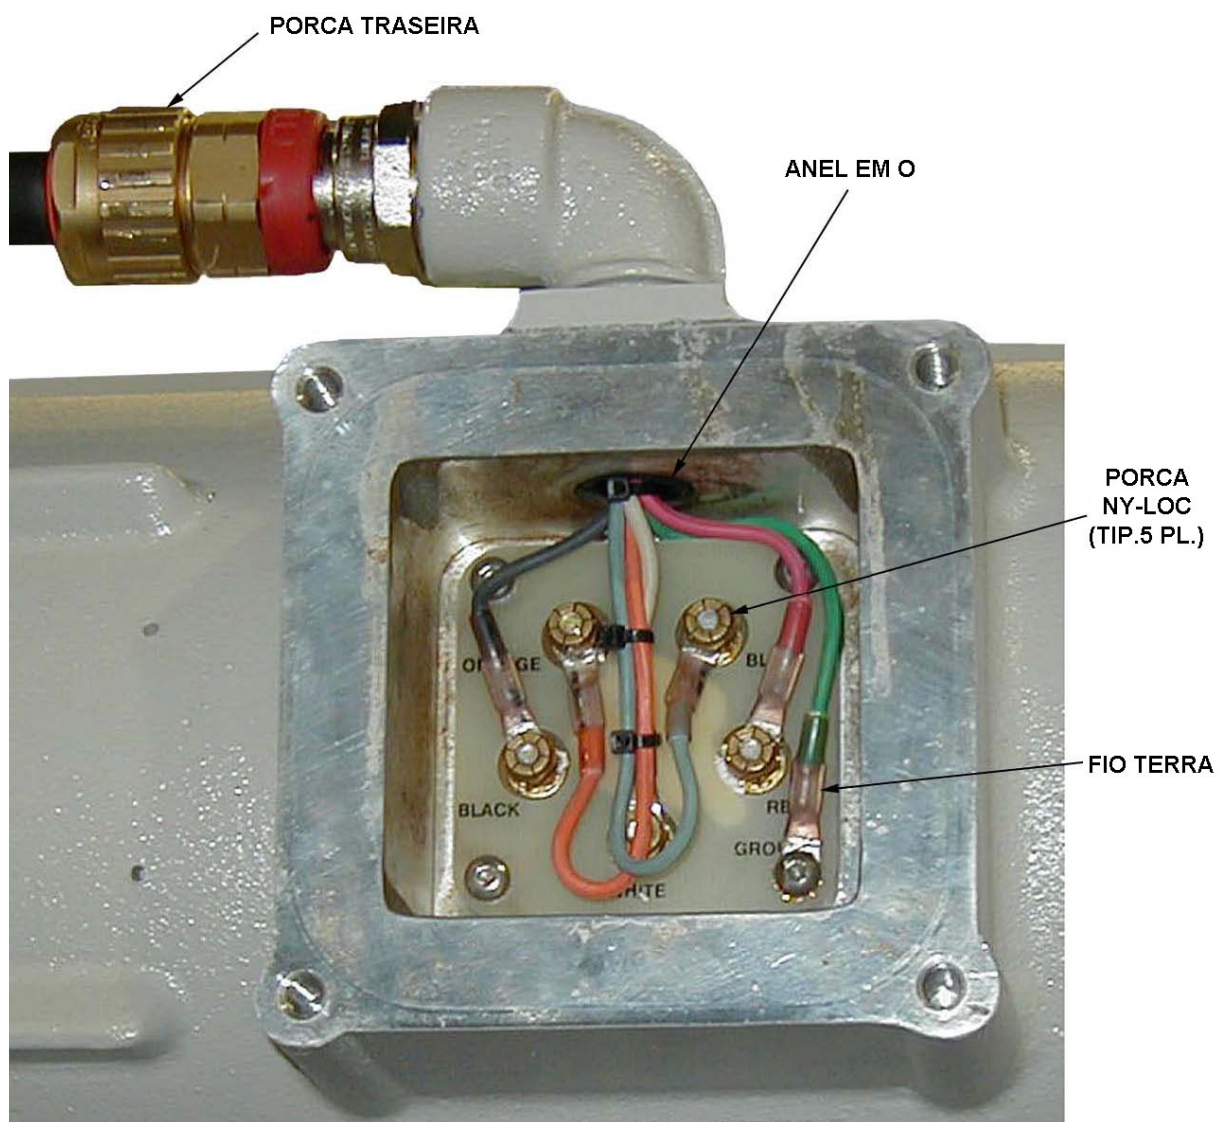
Conexões do cabo do motor ao bloco de terminais
